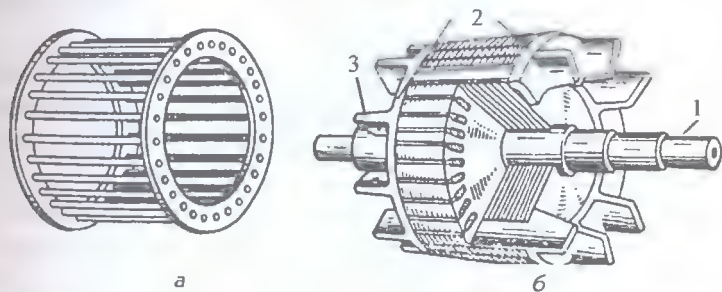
Короткозамкнутый ротор (обмотка — «беличья клетка» сварная (а), литая (б)): 1 — вал; 2 — короткозамыкающие кольца; 3 — вентиляционные лопатки
